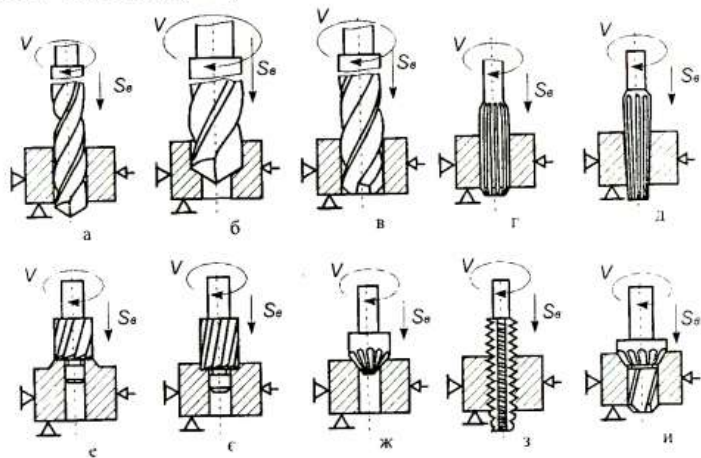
Схеми обробки отворів на свердлильних верстатах
